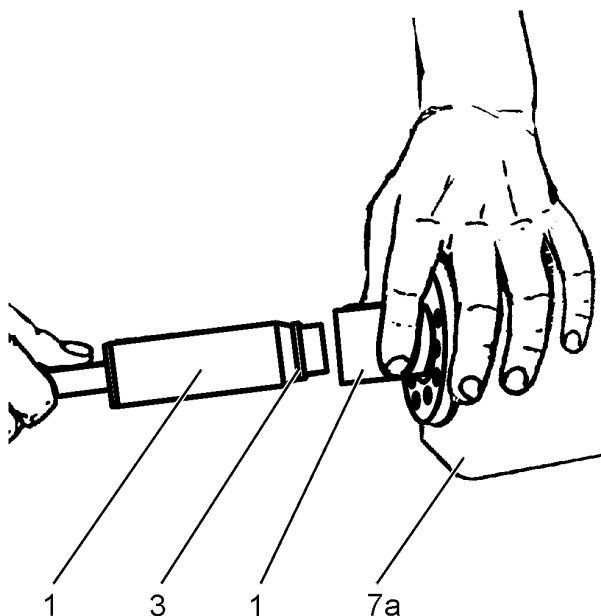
В.7С. Установка комплекта уплотнительных колец «O-ring/kin-ring»
